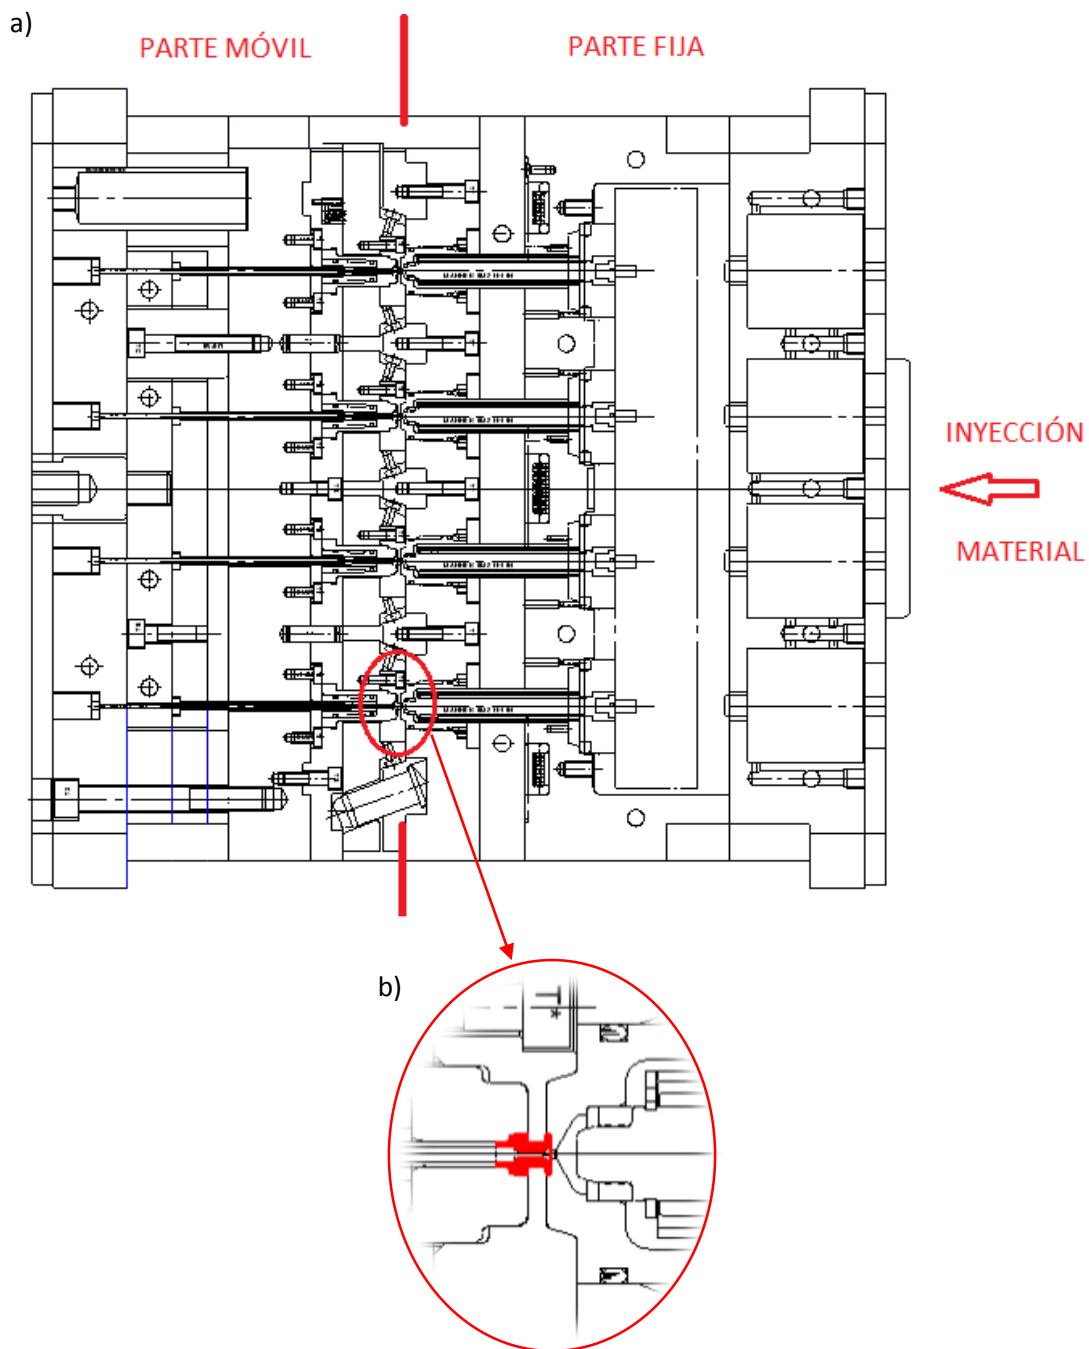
a) Disposición de la pieza en el molde; b) Detalle de la disposición de la pieza en el molde
